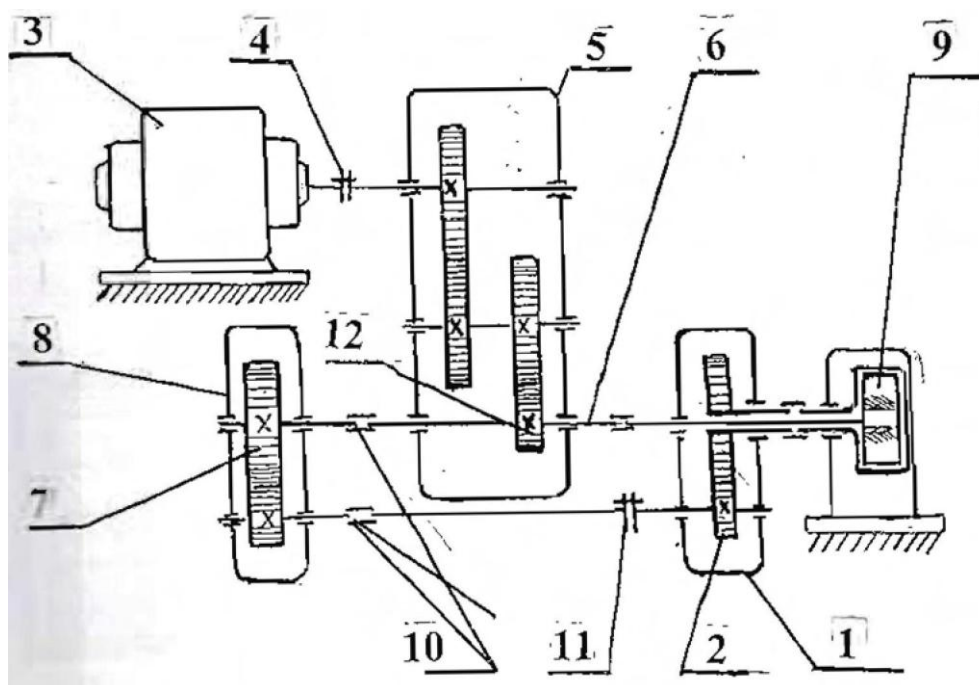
Кинематическая схема станда Ш-3:
